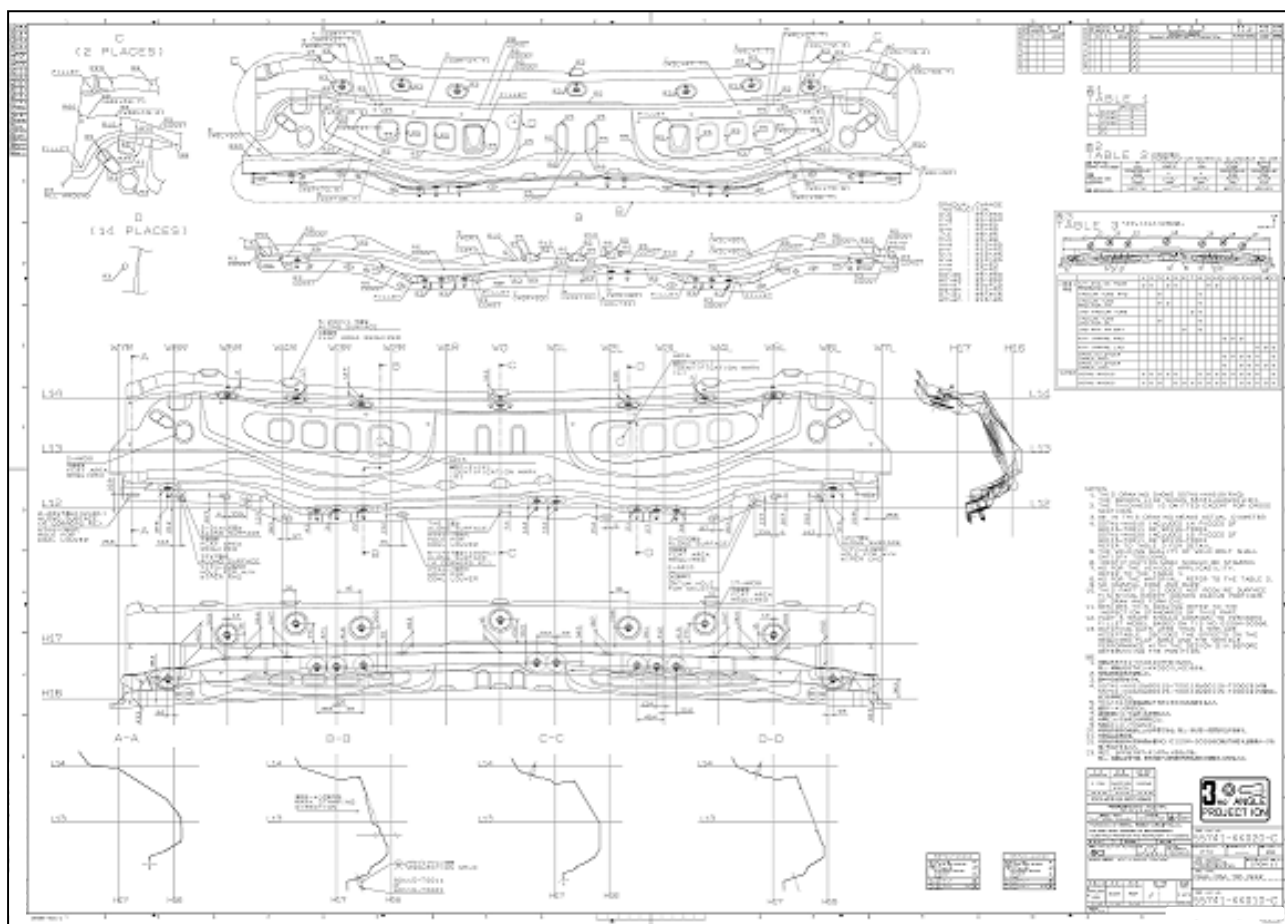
Plano de Diseño de un subconjunto estampado con tornillos soldados por proyección.
